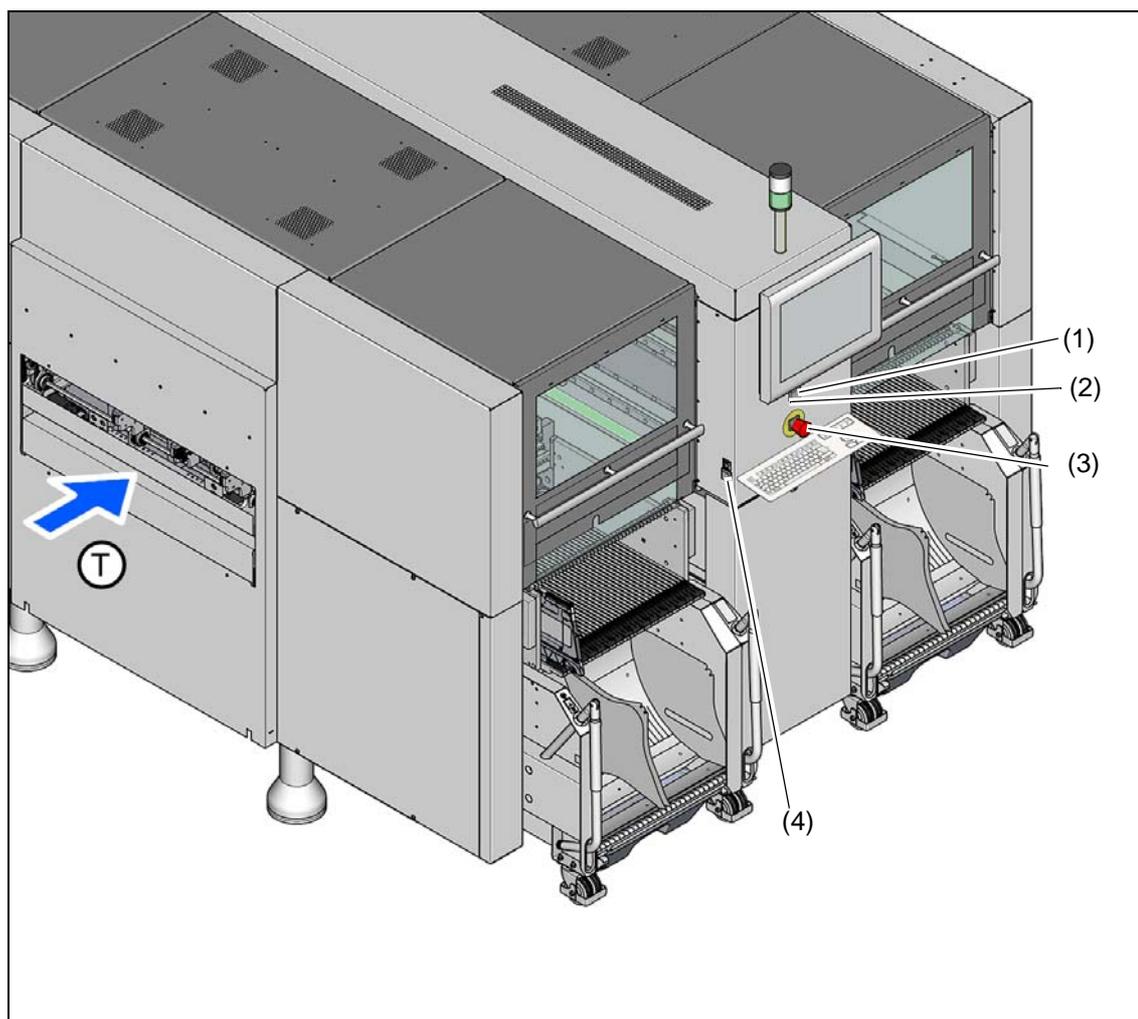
4 开关和按钮的位置 - PCB 输入侧视图 (示例为 SX4)
